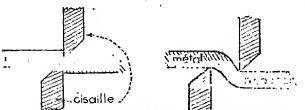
Les lames d'une cisaille doivent glisser l'une sur l'autre sans jeu (à gauche); sinon la feuille plie et n'est pas tranchée (à droite).
